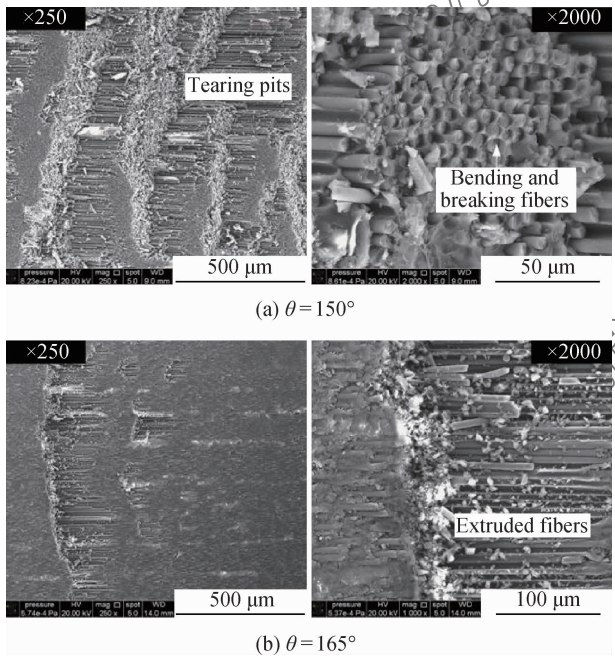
逆纤维方向角下 CFRP 单向层合板的切削表面形貌
